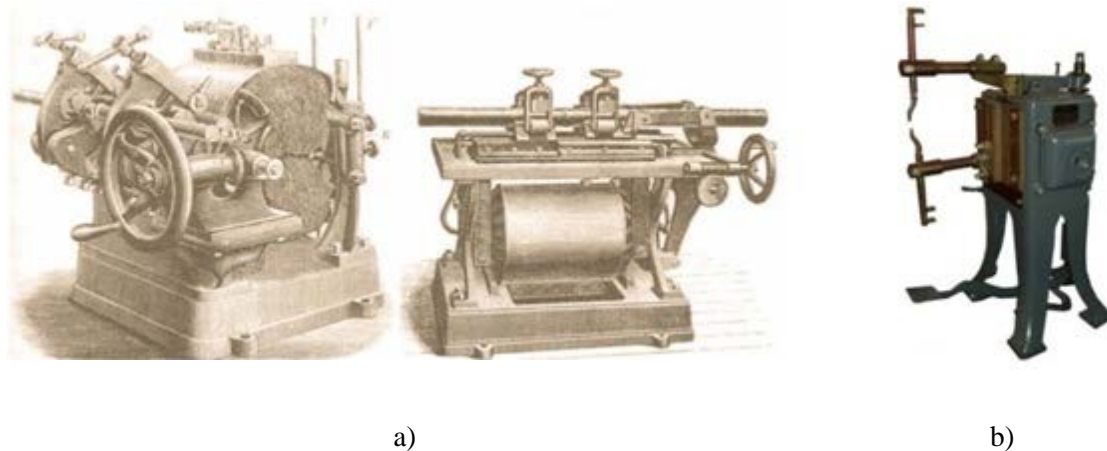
Máquinas de soldadura por resistência [2]: a) Máquina de soldadura por resistência topo a topo b) Máquina de soldadura por resistência por pontos
